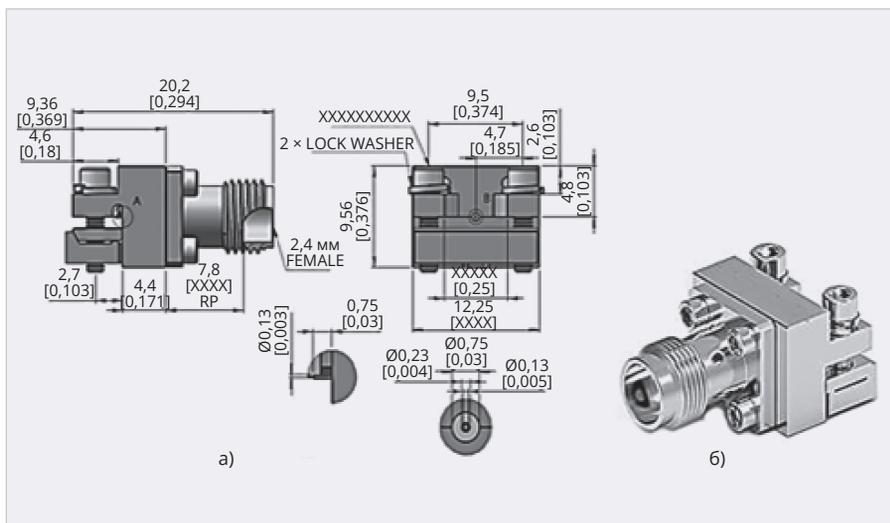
Концевой соединитель 2,4-KFDEL13 для установки без пайки на печатные платы: конструкция (а), внешний вид (б)
